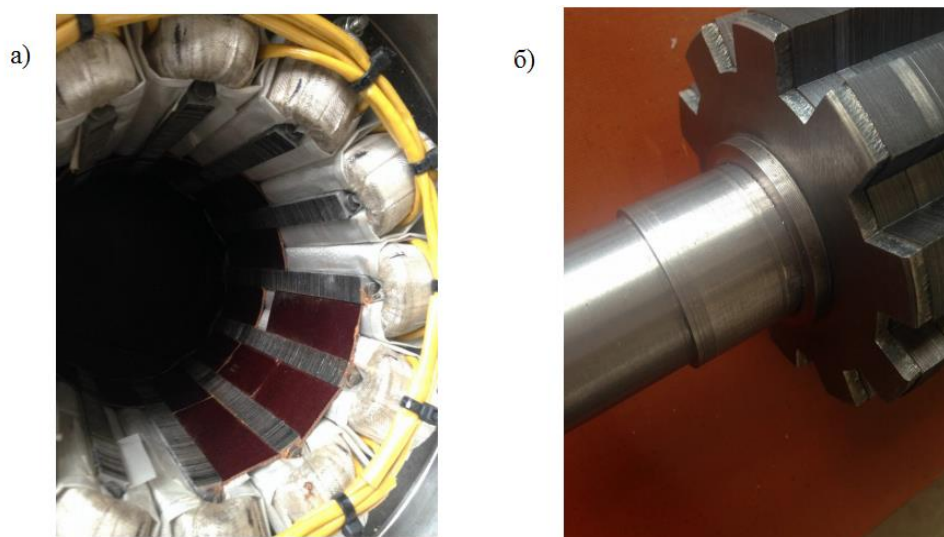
а) внешний вид статора, б) внешний вид ротора вентильно-индукторной машины
